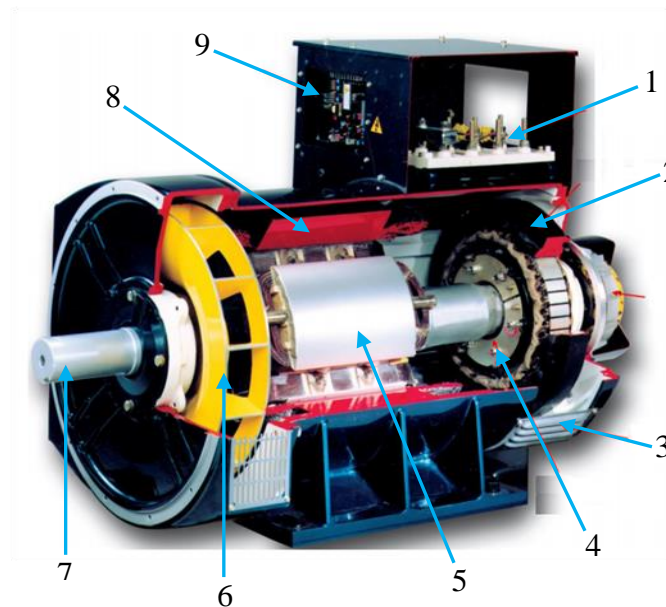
Machine synchrone à rotor bobine (Alternateur) : 1- Plaque à borne, 2- Excitation, 3- Cage, 4- Redresseur, 5- Rotor bobine, 6- Ventilateur de bout d'arbre, 7- Arbre, 8- Bobine statorique, 9- Régulateur automatique de tension.
